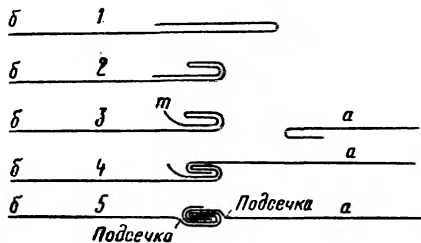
Заготовка полуторного фальца по способу П. А. Лапшова
